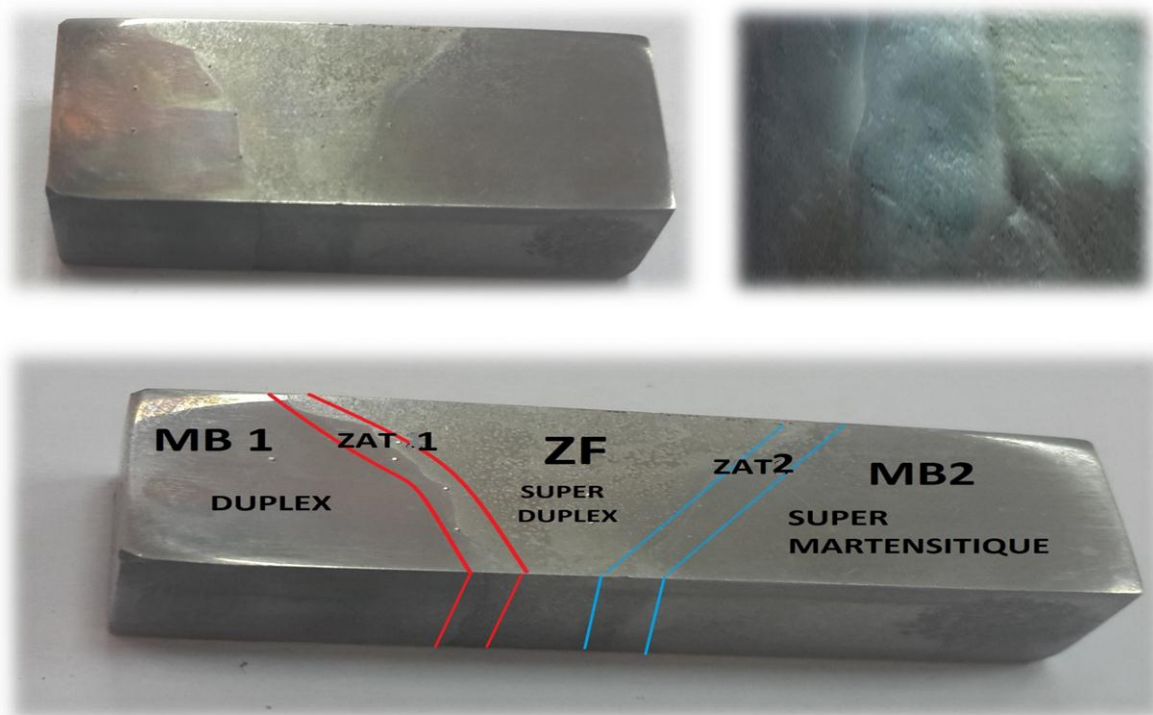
Illustration macrographique du joint soudé et des zones principales.
